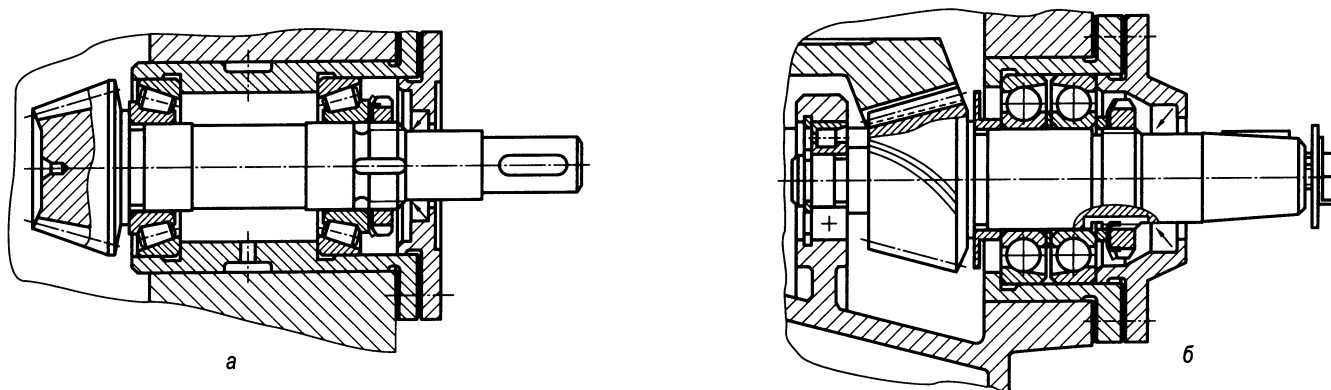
Вал-шестерня конической зубчатой передачи с консольным (а) и неконсольным (б) расположением шестерни
